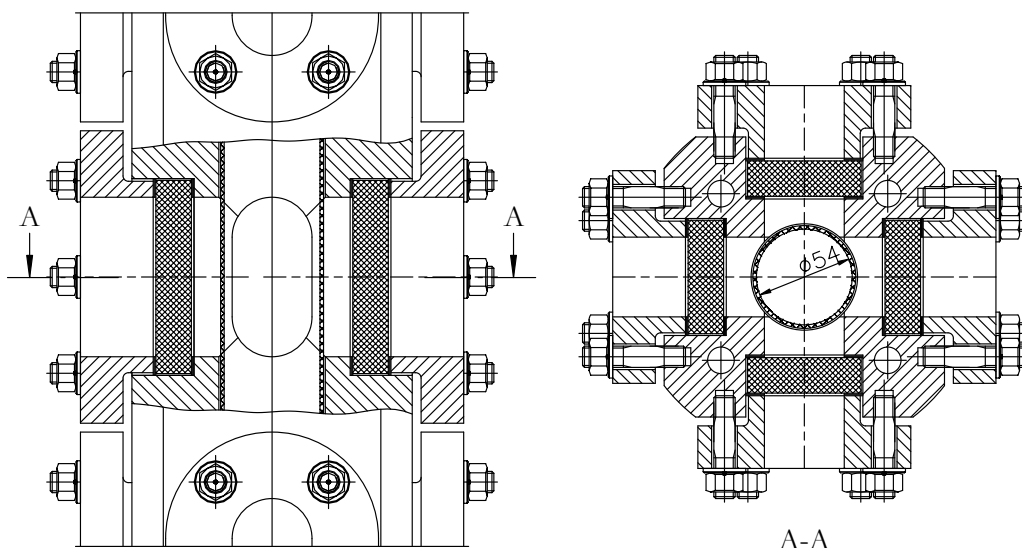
Ausschnitt des Hochdruckblasensäulenreaktors. Links: Ausschnitt um ein Sichtfenster, rechts: Querschnitt entlang einer Ebene mit Sichtfenstern.
